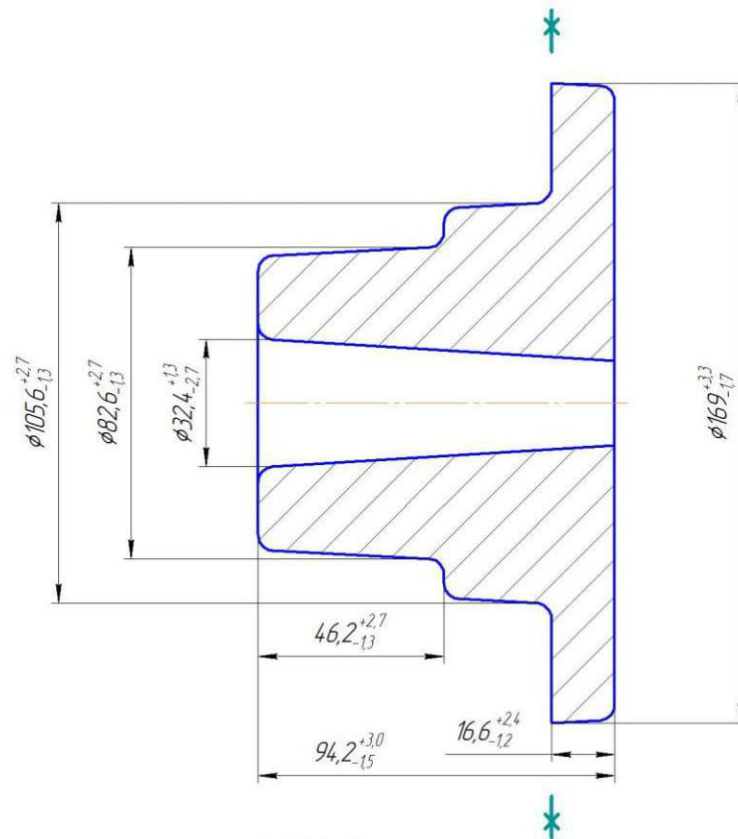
Виготовлення заготовки штампуванням на ГКМ
